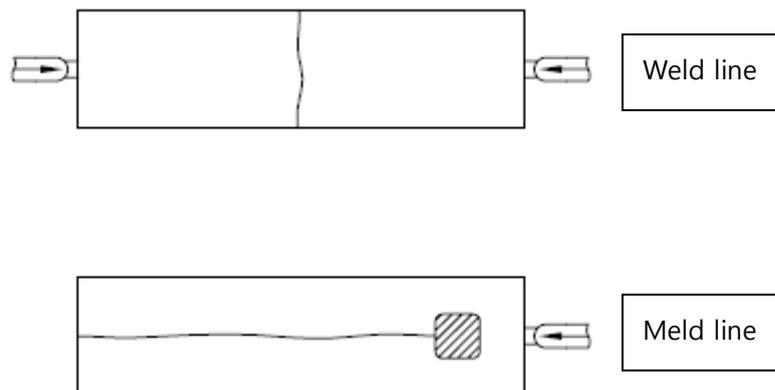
Weld의 Type(weld line 및 meld line)
